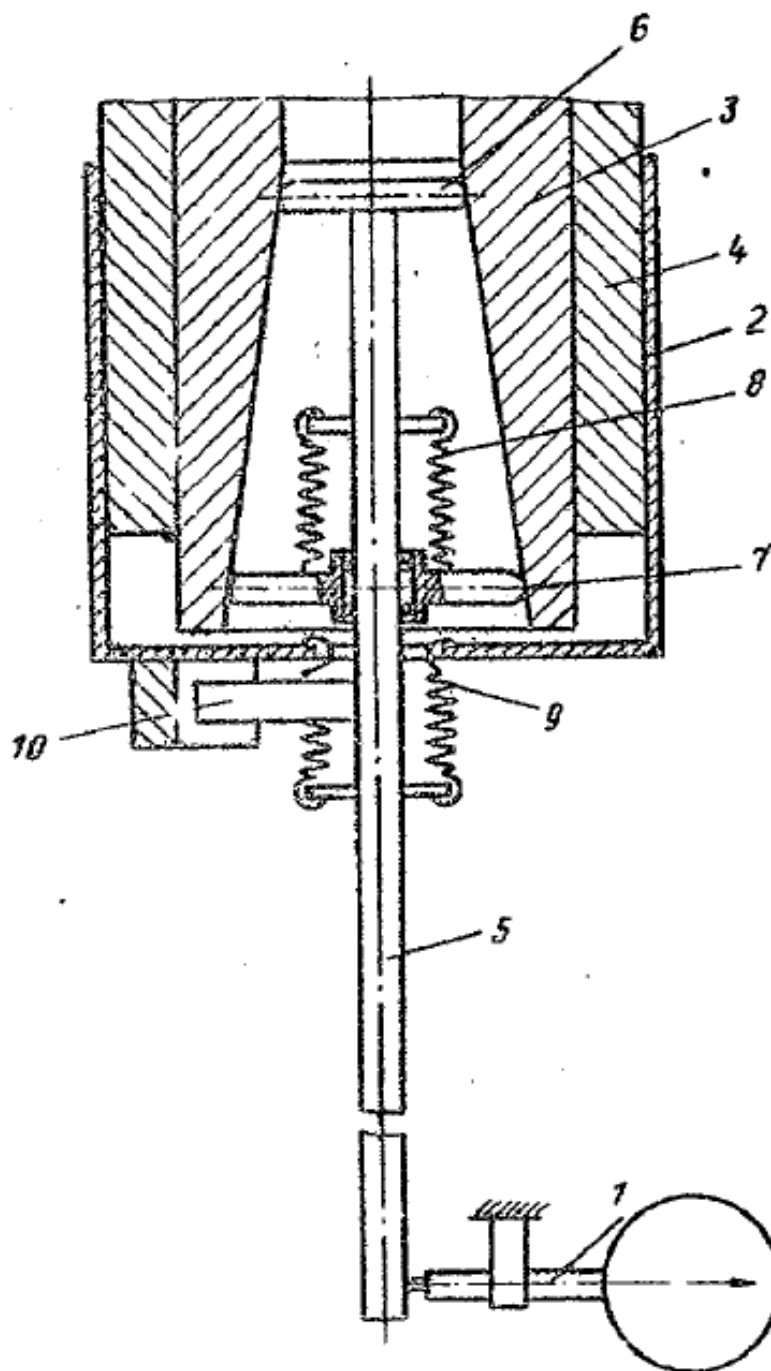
Пристрій для вимірювання внутрішніх конусів
